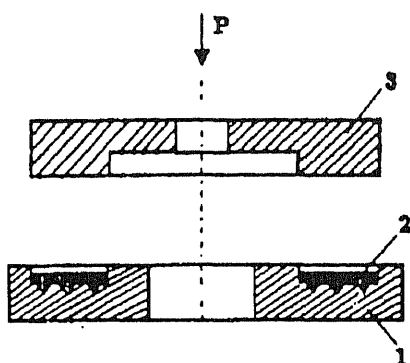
Схема прессования шихты в кольцевом пазу заготовки
